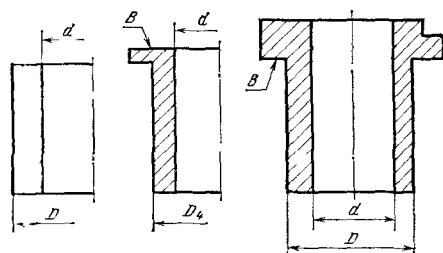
Схемы для определения допусков формы и расположения поверхностей кондукторных втулок
